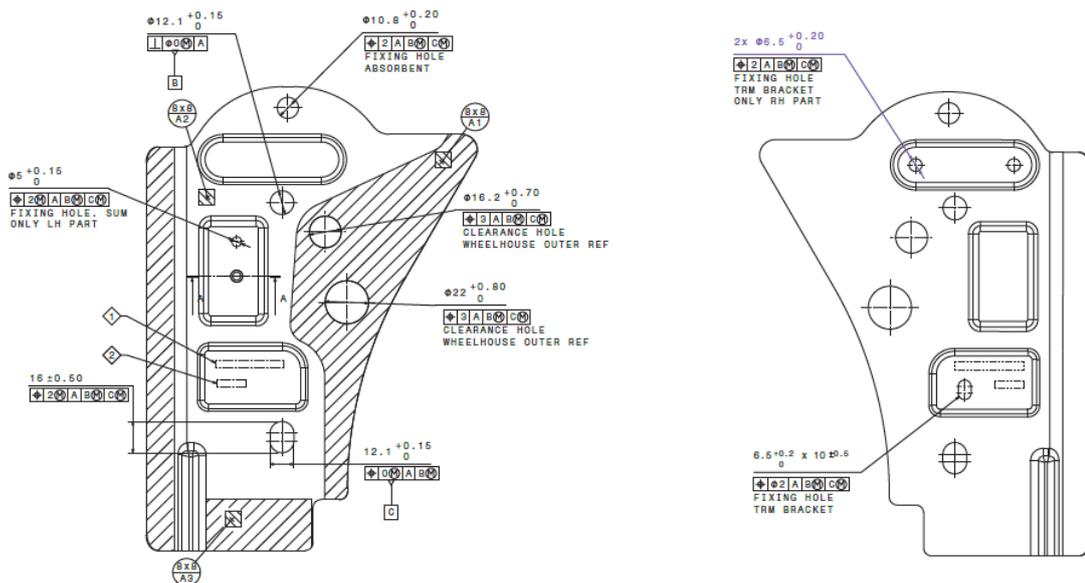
Plano de la pieza detallando las tolerancias
